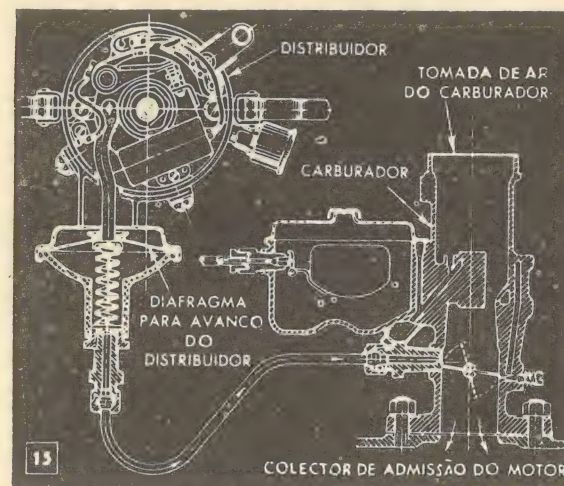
Corte do distribuidor e carburador mostrando o avanço automático por depressão
